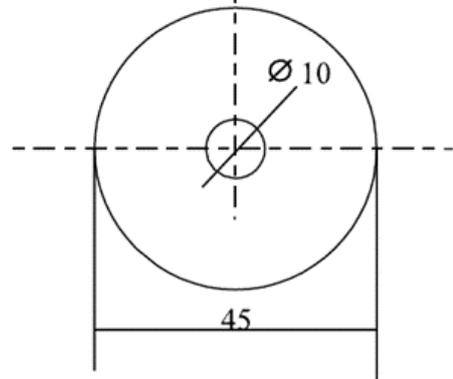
Sobrecarga anelar padrão 490 g (dimensões em milímetros)
